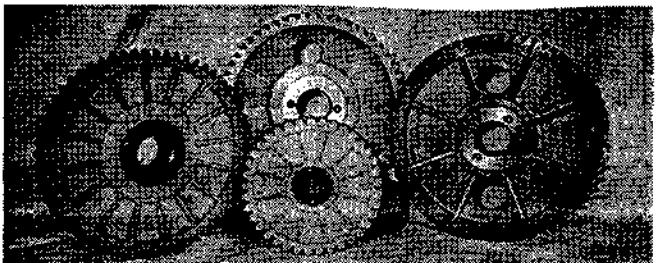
Зубчатые колеса из стеклонаполненного полиамида 6 для ДВС
